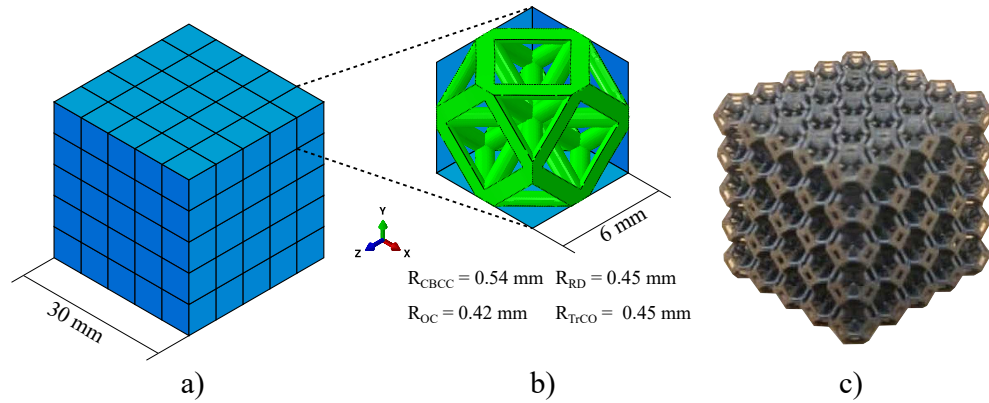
Géométrie des éprouvettes lattices : a) dimensions globales, b) dimensions de chaque VER et c) représentation réelle d'une éprouvette (TrCO)
